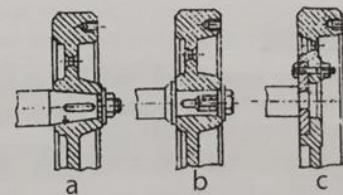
Montarea volanților: a - pe con; b - pe fus cilindric; c - cu flanșă și șuruburi.
